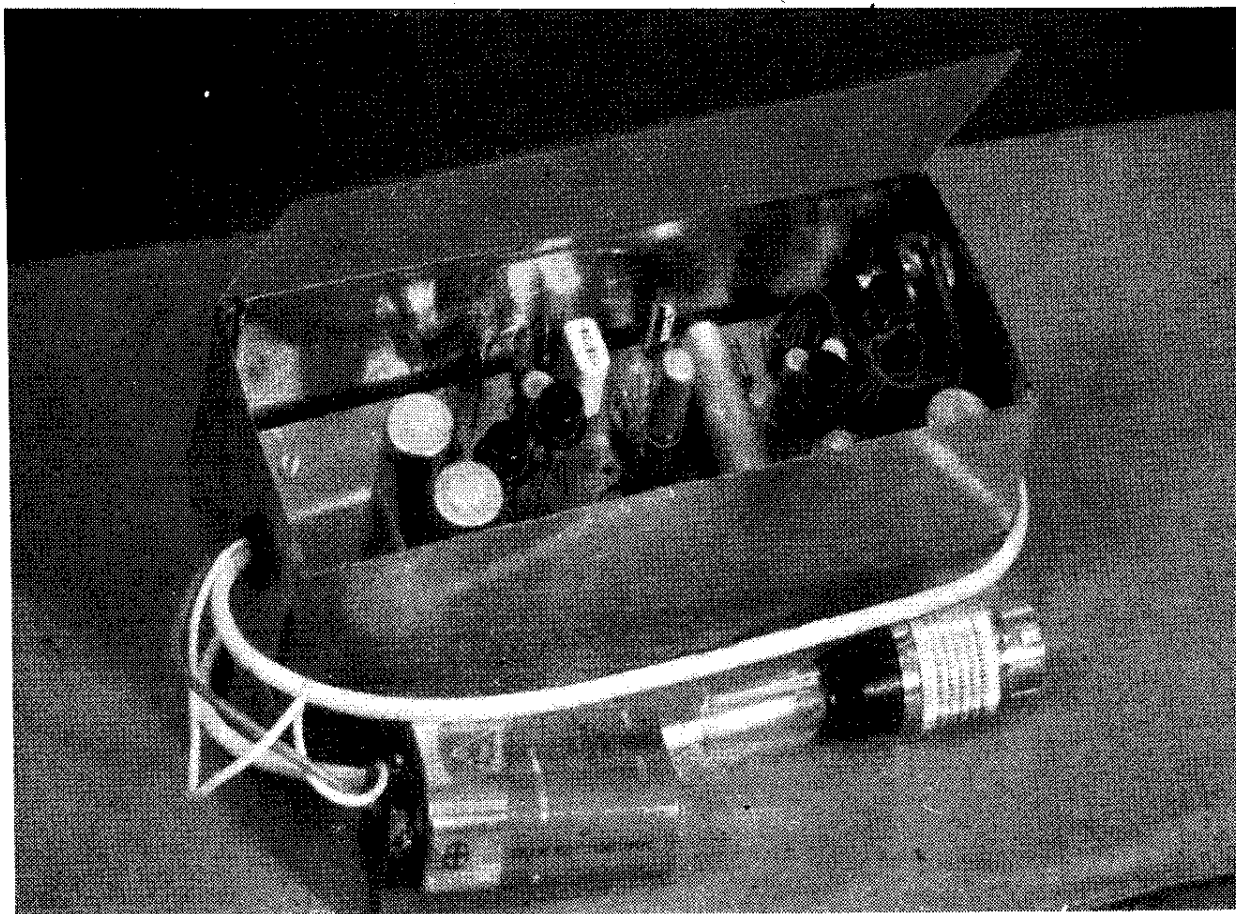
Osazená destička s plošnými spoji podle obr. 73
